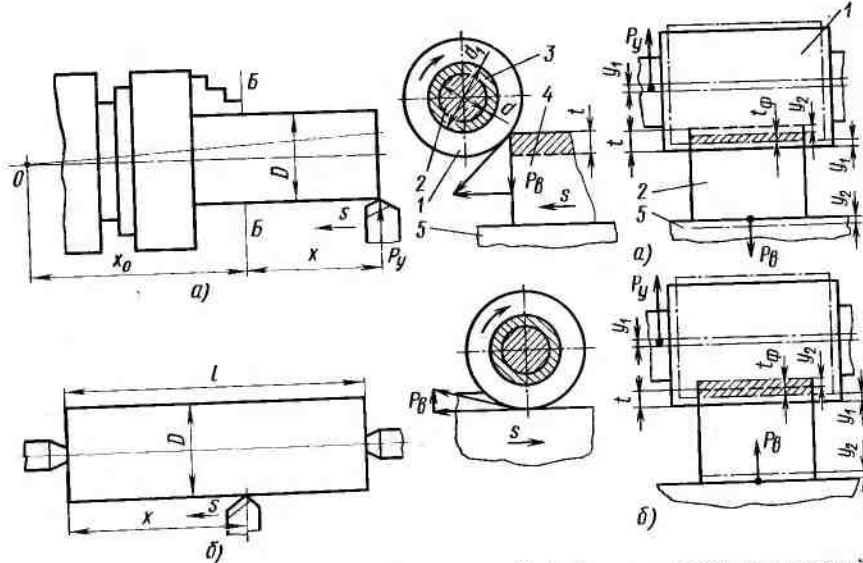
Схема определения податливости динамической системы при закреплении заготовки в патроне (а) и в центрах (б) Рис. 11.8. Схема упругих перемещений при порубном (а) и встречном (б) фрезеровании цилиндрической фрезой
